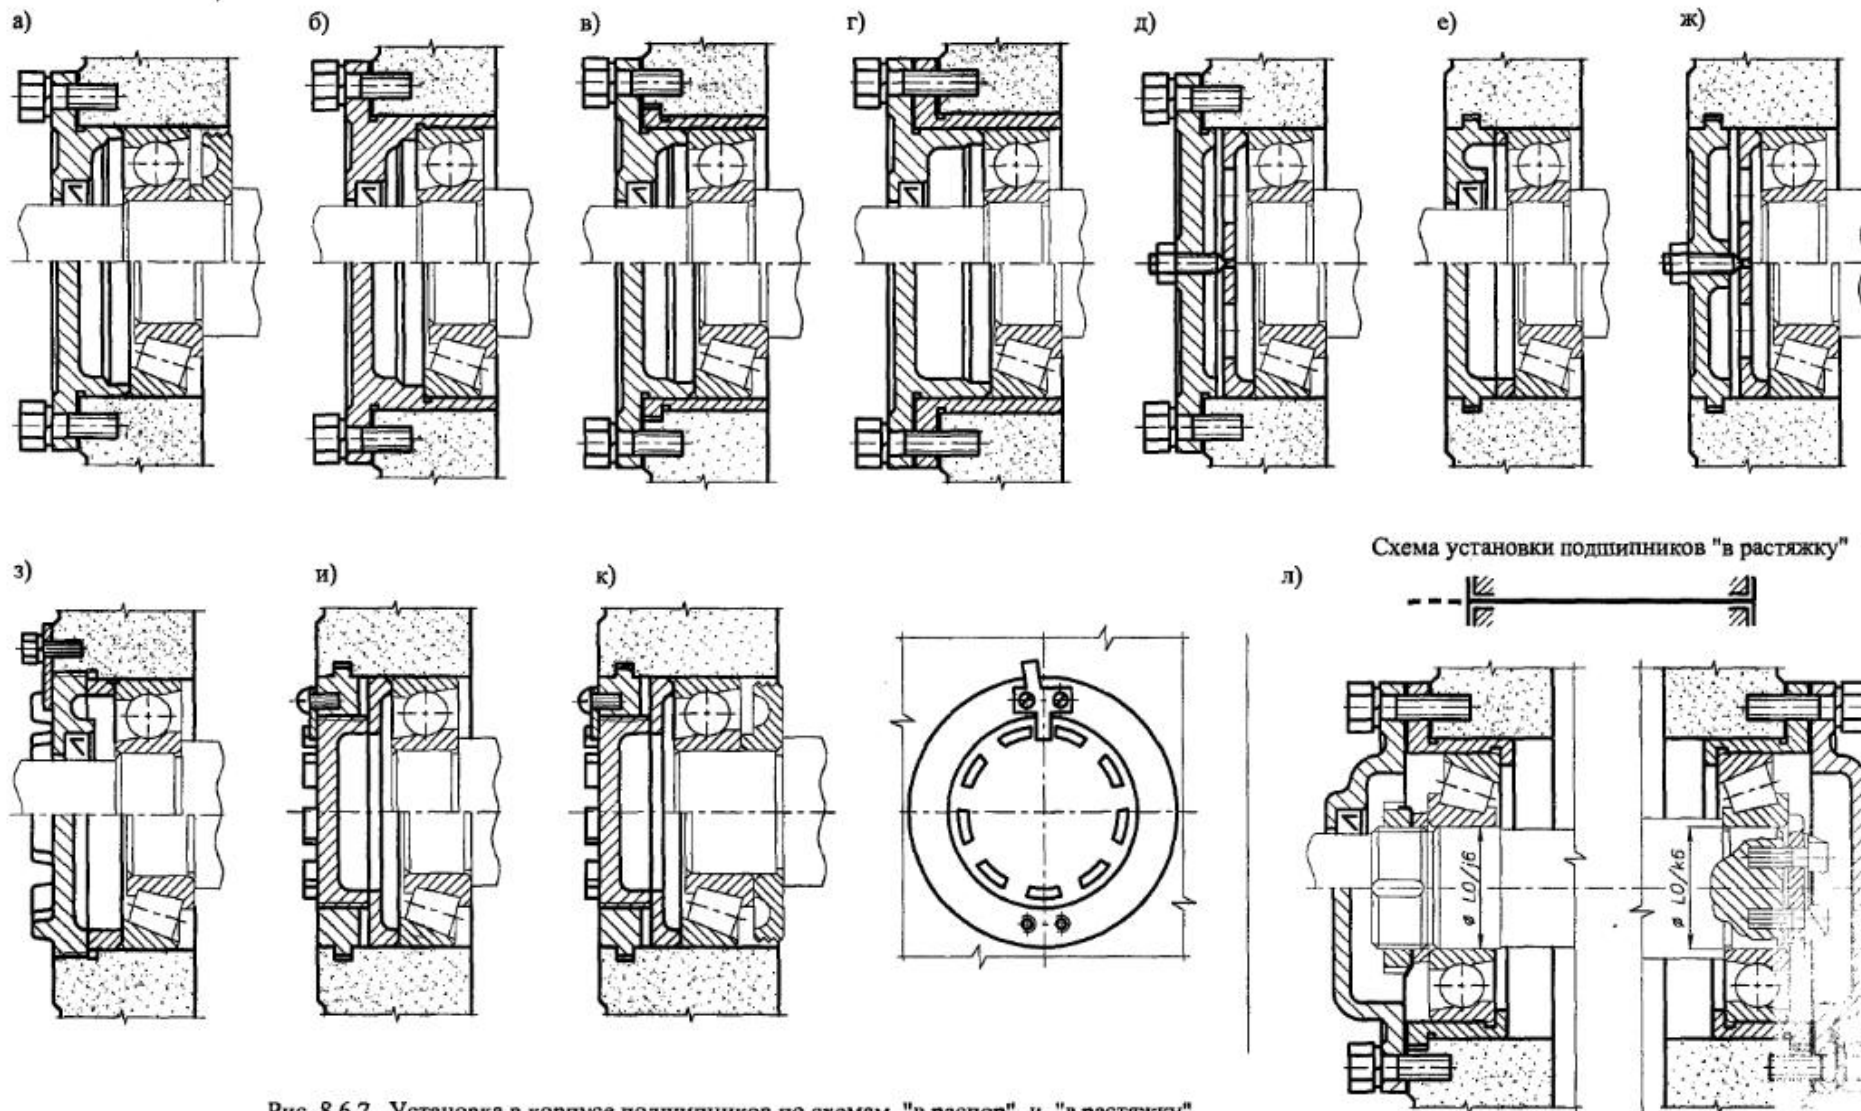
Установка в корпусе подшипников по схемам "в распор" и "в растяжку"
